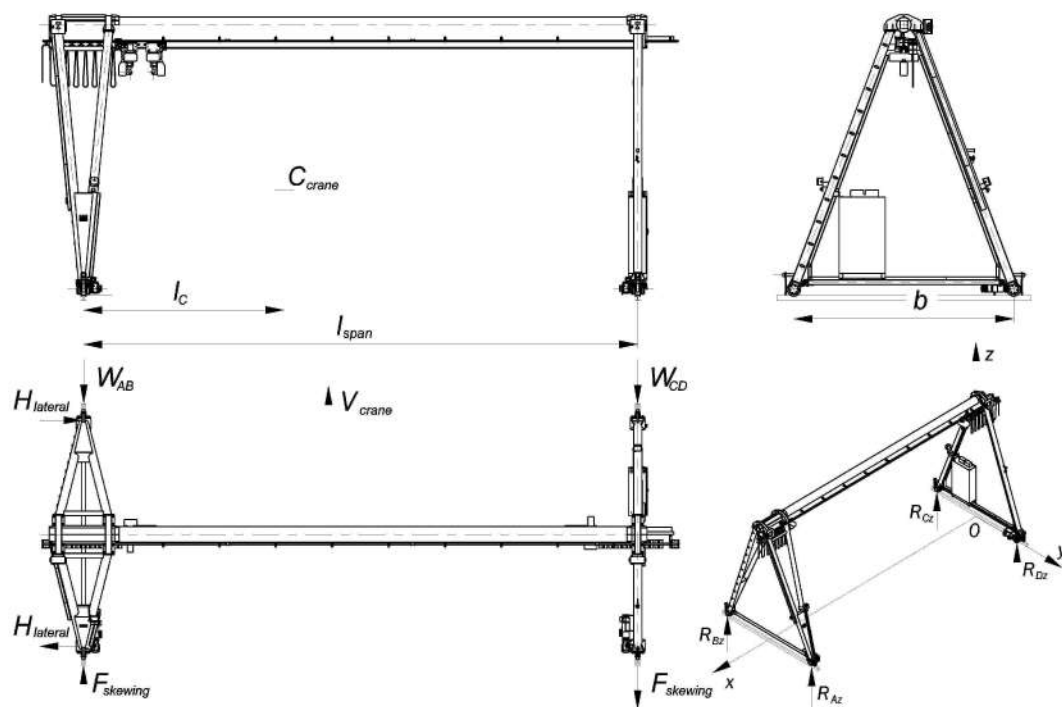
Общий вид козлового крана с расчетной схемой нагрузок при перекосе
